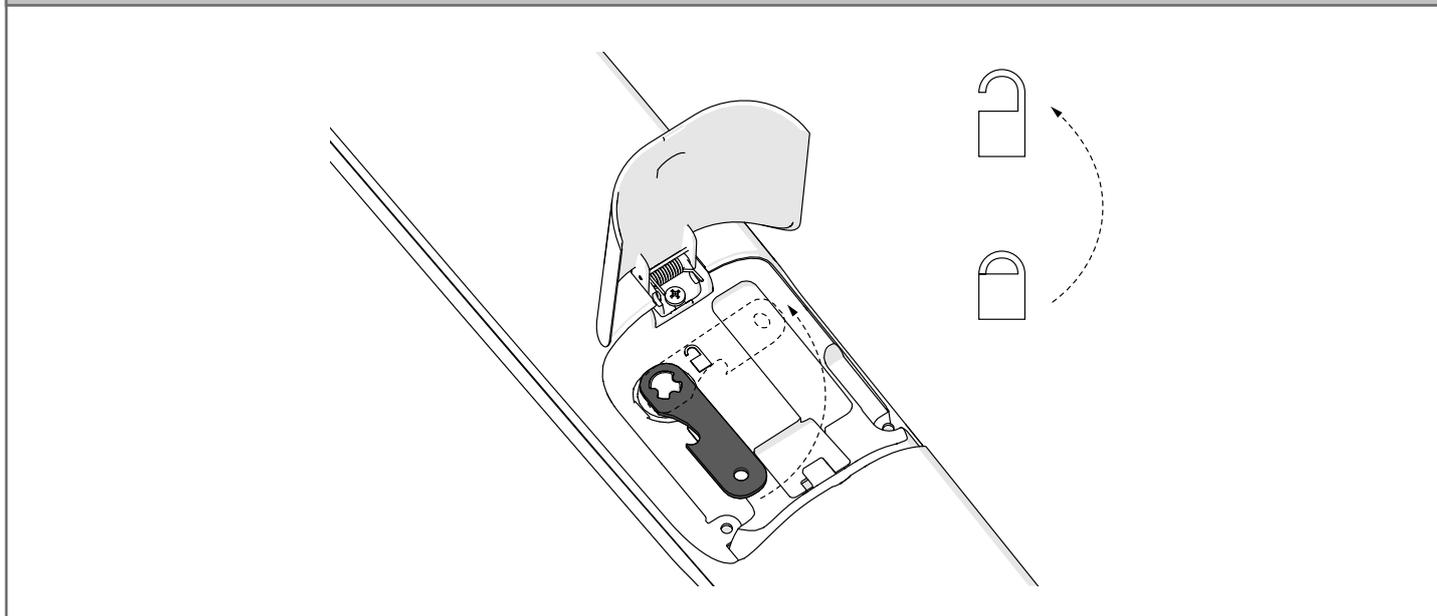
FR - Fixation du motoréducteur et du chevron arrière
